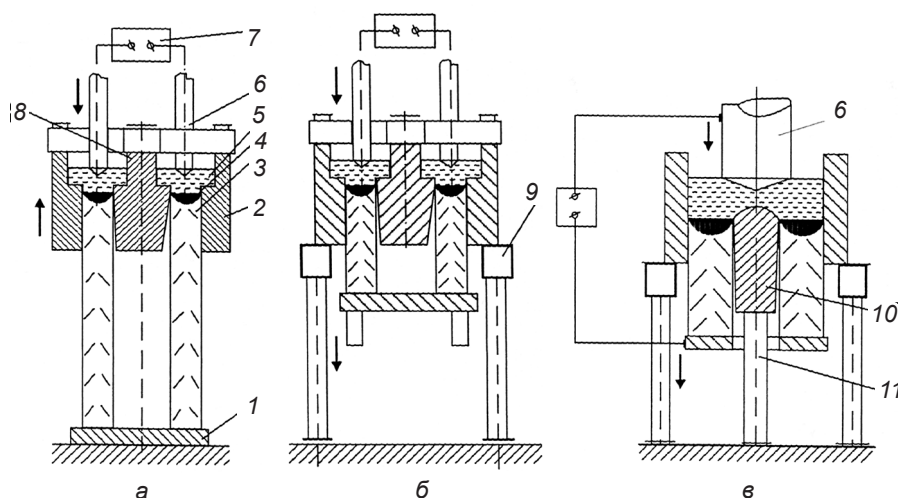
Схемы ЭШЛ с относительным перемещением кристаллизаторов и выплавляемых полых заготовок: с неподвижной заготовкой и перемещающимся вверх блоком кристаллизаторов (а), с неподвижным блоком кристаллизаторов и перемещающейся вниз заготовкой (б), с перемещающейся вниз заготовкой и неподвижным наружным и подвижным дорном (в); 1 – поддон, 2 – кристаллизатор, 3 – заготовка, 4 – металлическая ванна, 5 – шлаковая ванна, 6 – расходный электрод, 7 – источник тока, 8 – подвижный дорн, 9 – опора, 10 – неподвижный дорн, 11 – шток
